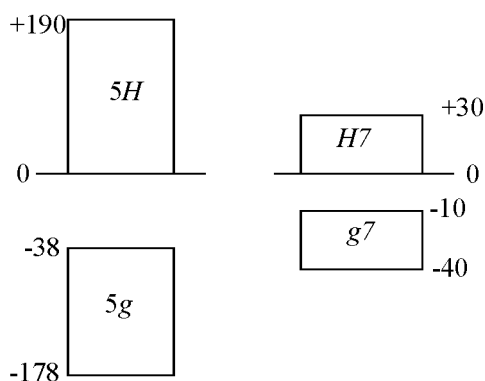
Схема расположения полей допусков гладких и резьбовых поверхностей
